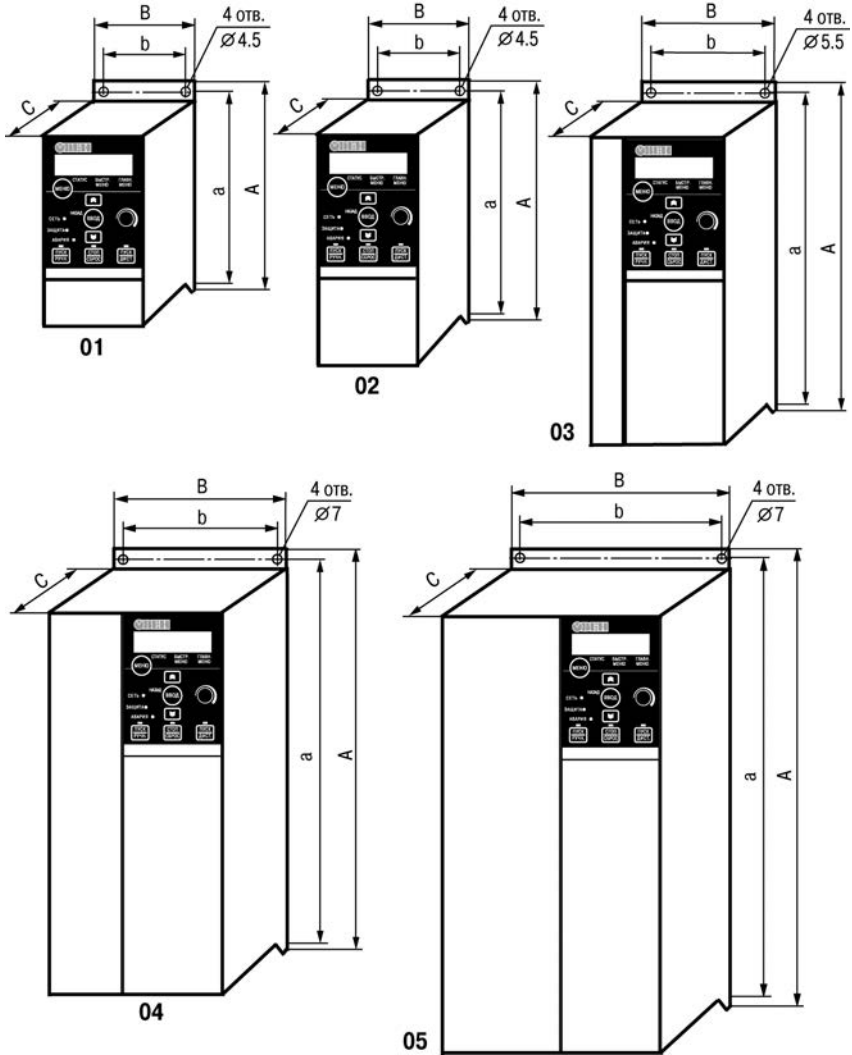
Габаритные и присоединительные размеры прибора для типов корпуса 01 – 05
